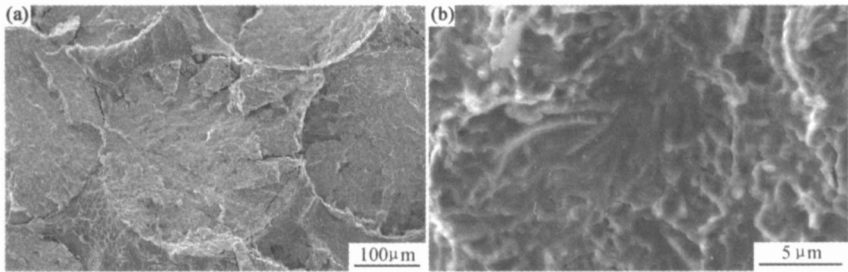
动态拉伸断口形貌 (a) 低倍断口形貌; (b) 钨丝解理断裂形貌
